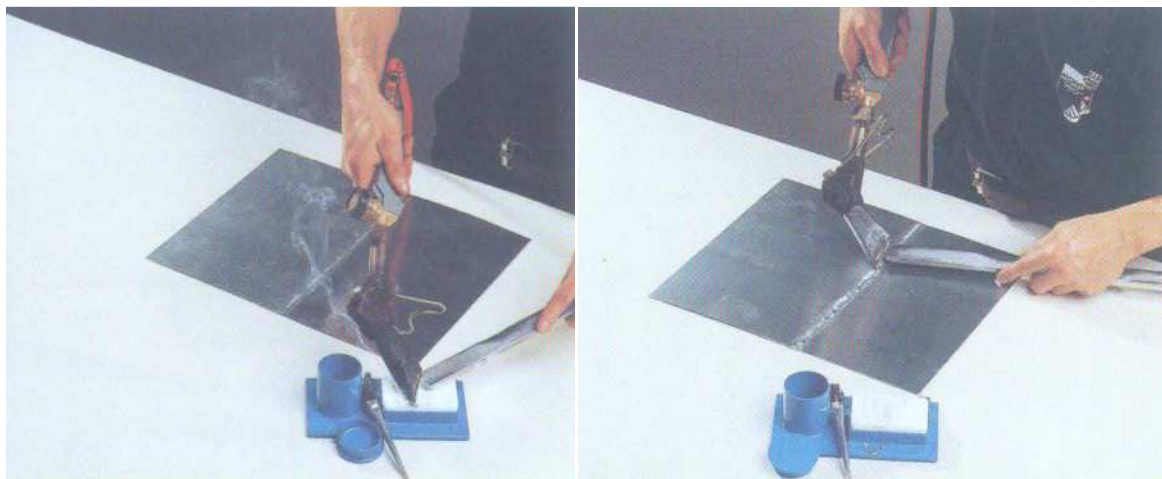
Utilização de aparelho de soldar para derreter barra de solda
